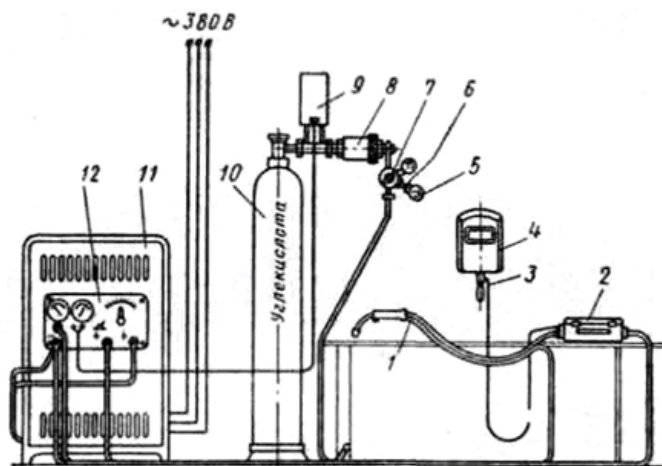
Схема поста А-547Р для полуавтоматической сварки в среде углекислого газа проволокой диаметром 0,8 — 1,0 мм: 1 — газопровод; 2 — подающий механизм; 3 — кнопка включения; 4 — щиток для защиты дуги; 5 — манометр на 6 ат; 6 — переходный штуцер для установки манометра; 7 — редуктор кислородный; 8 — осушитель газа (на случай работы с неосушенной углекислотой); 9 — подогреватель газа; 10 — баллон с жидкой углекислотой; 11 — источник сварочного тока (выпрямитель или генератор); 12 — пульт управления
